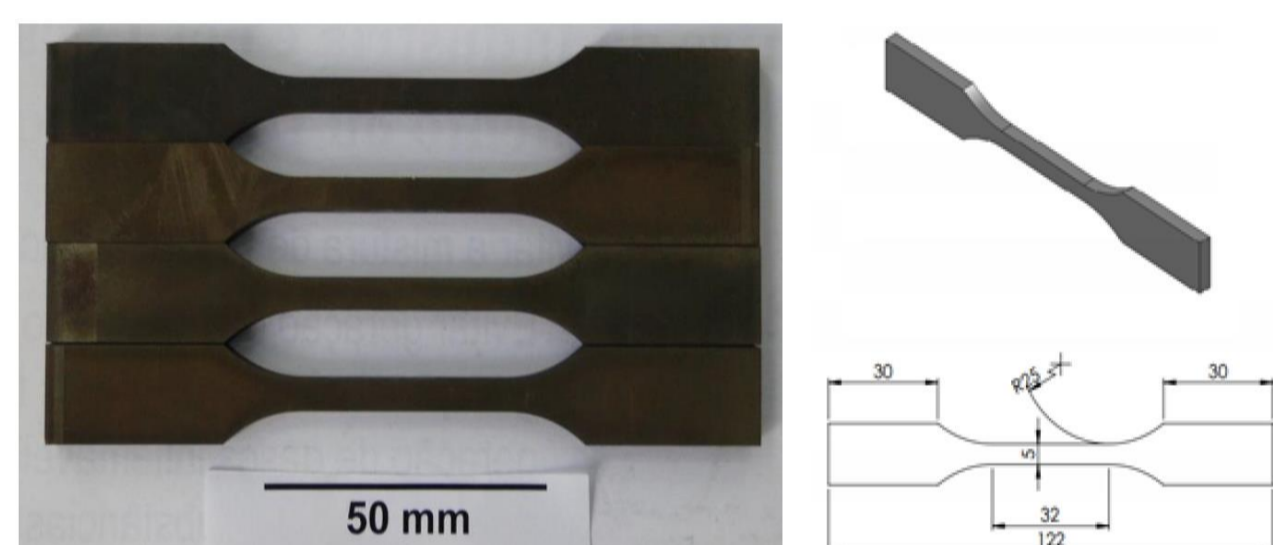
a) corpo de prova real; b) corpo de prova com duas dimensões.
